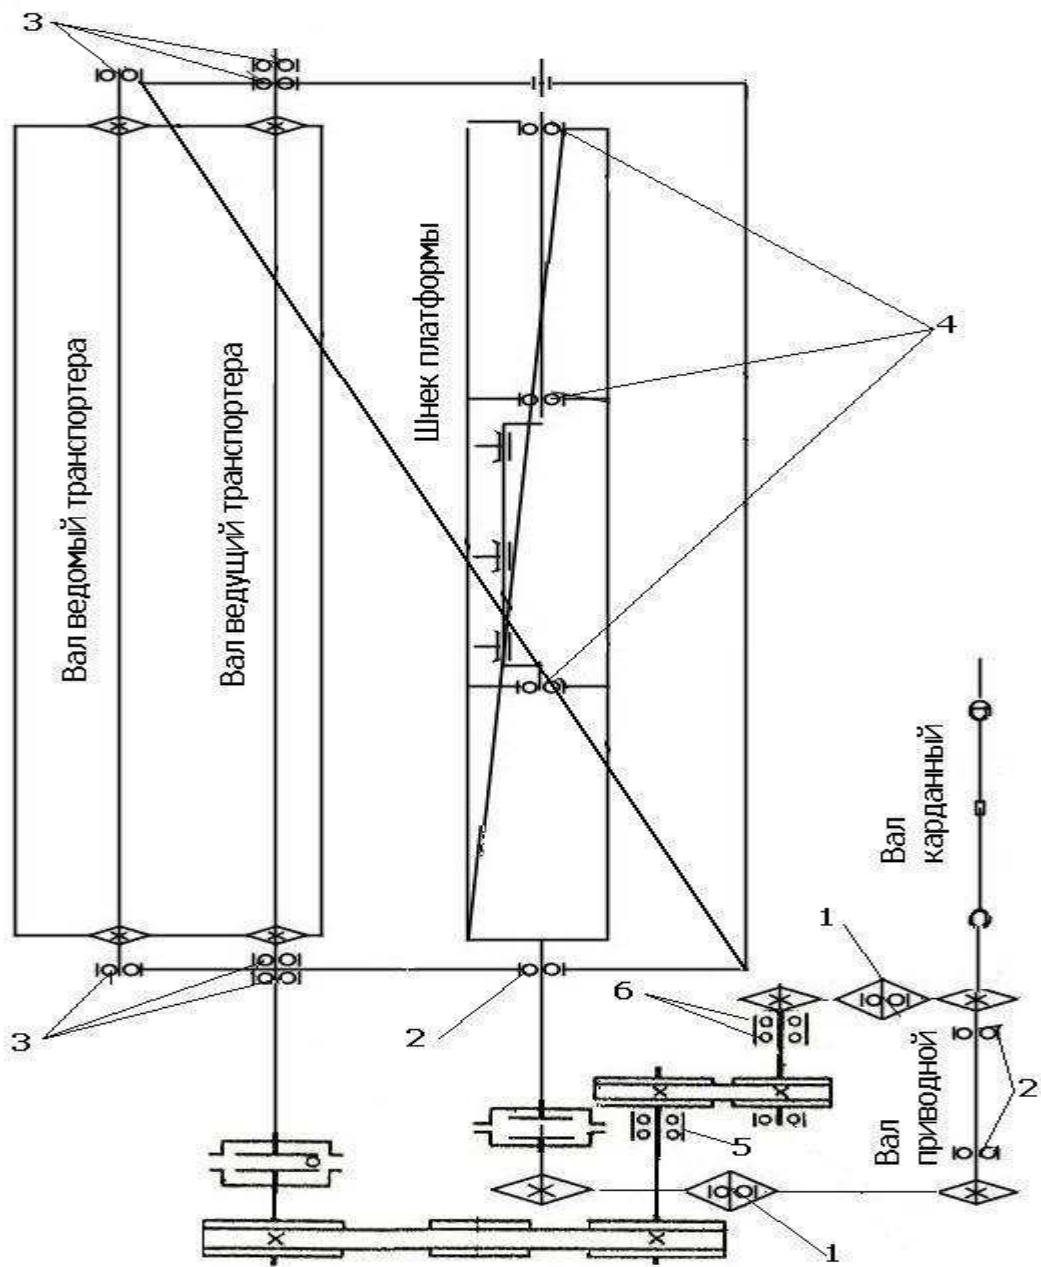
Схема расположения подшипников платформы-подборщика (вариаторная)
